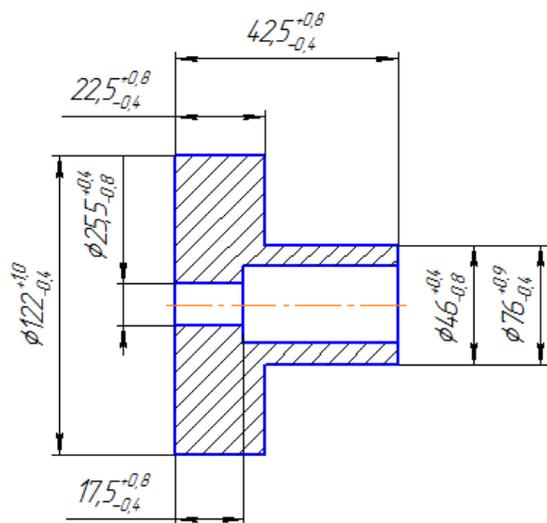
Эскизы заготовки и комплексной операции обработки детали «Корпус»
